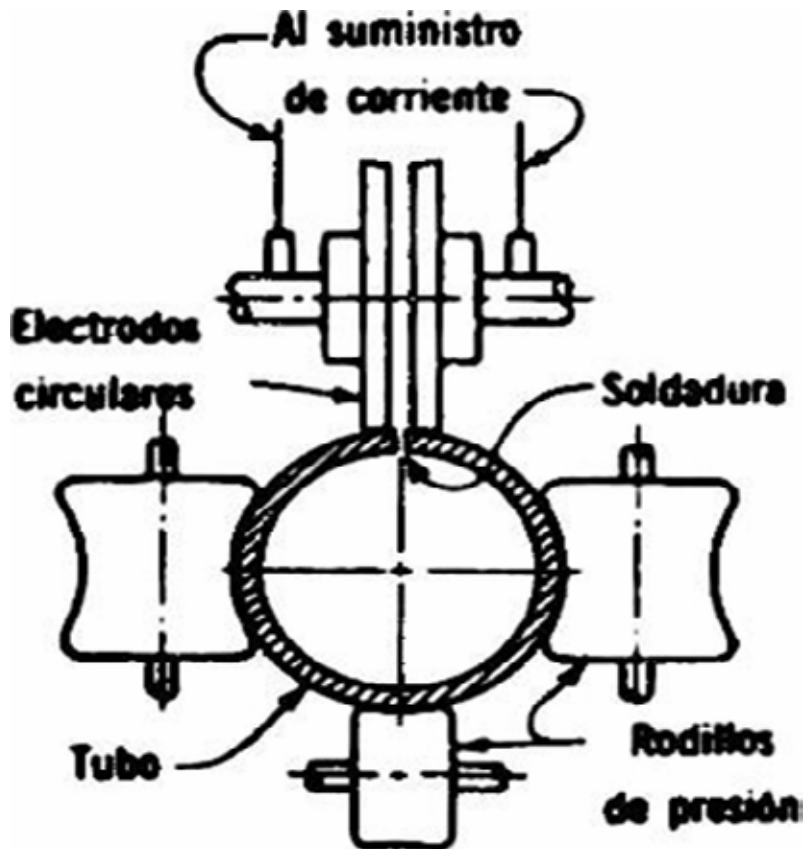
Soldadura Continua a Tope Por Resistencia Para Tubo de Acero
